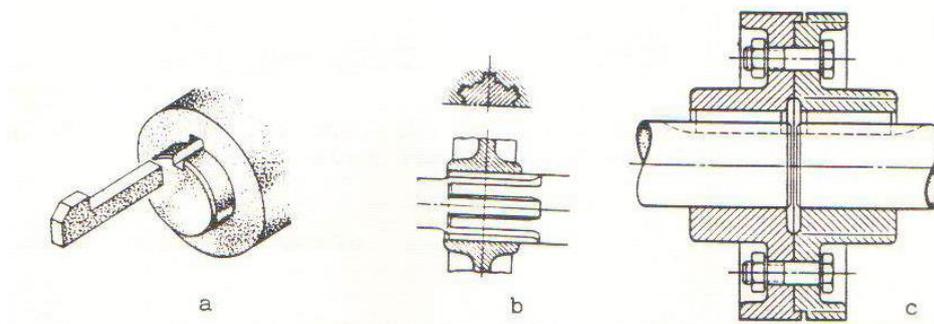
Acoplamento rígido com chaveta (a); árvore estriada (b); flanges (c)
